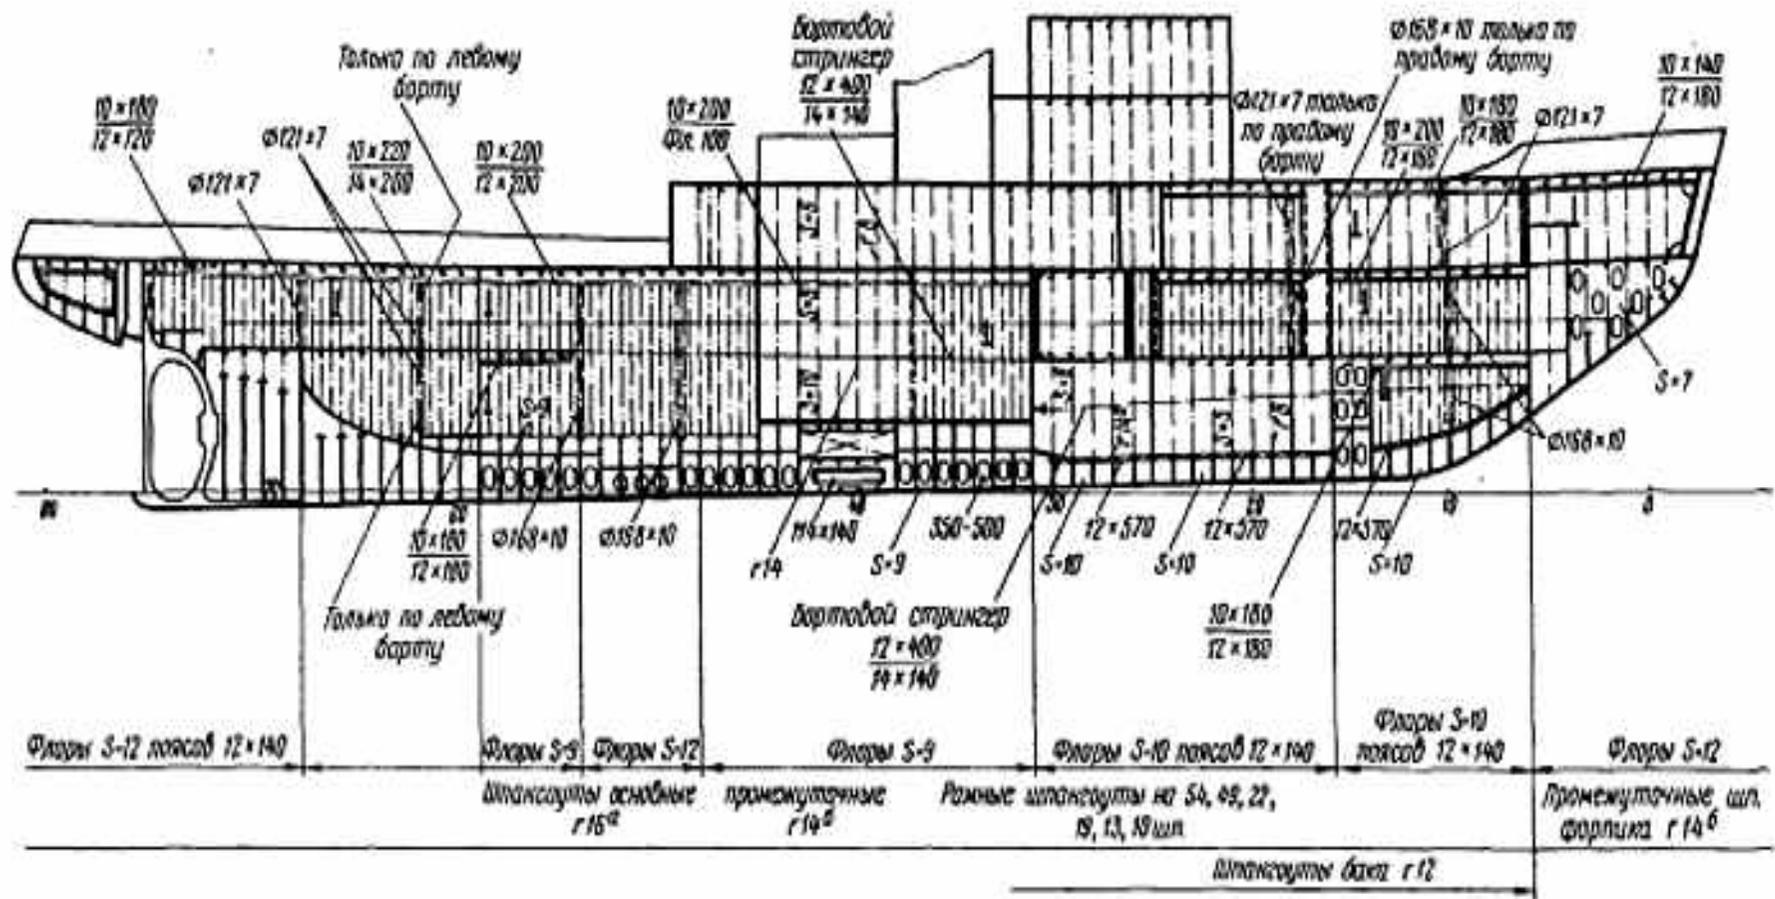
Конструктивный продольный разрез корпуса по диаметральной плоскости
